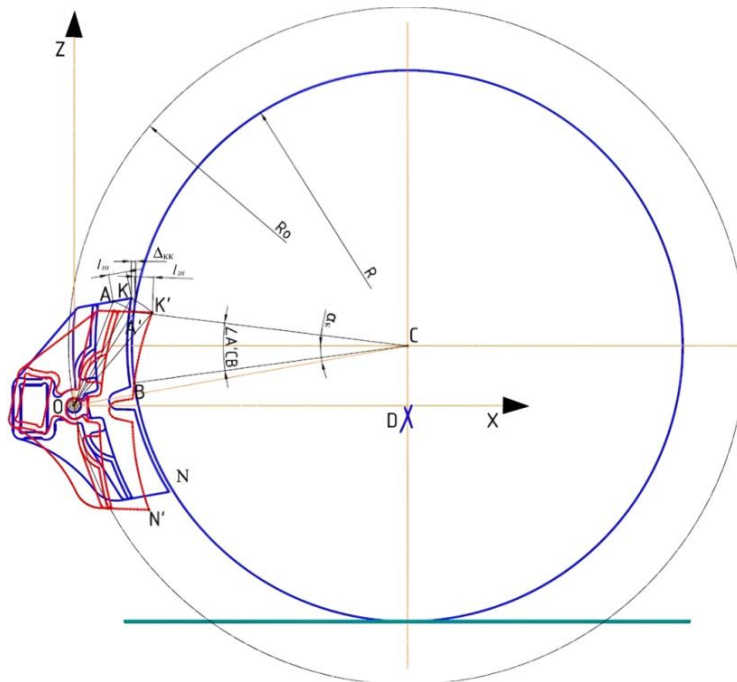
Розрахункова схема обертання ГБ з колодкою
